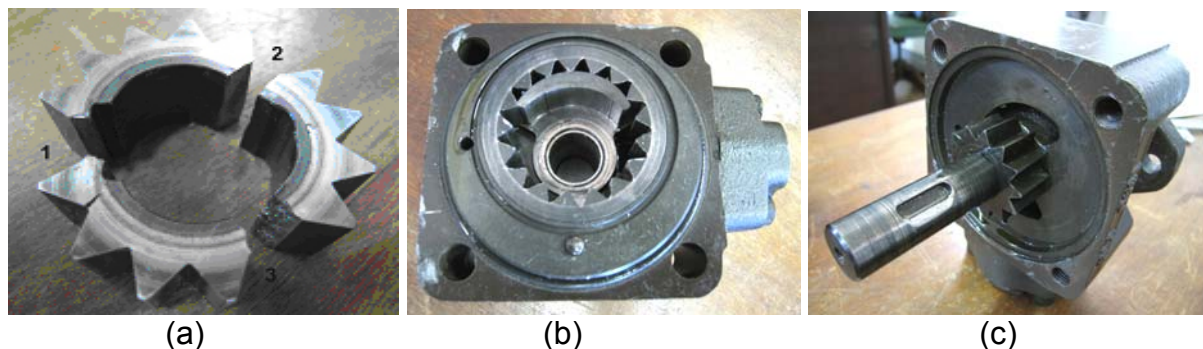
Detalhes da bomba. (a) Engrenagem interna fraturada em três posições. Os números “1”, “2” e “3” indicam a seqüência de trincamento. (b) Engrenagem externa travada, e “meia-lua” e bucha desgastados. (c) Eixo com chaveta desgastada.
